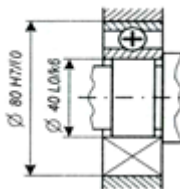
Обозначение посадочных мест подшипников качения на сборочном чертеже
